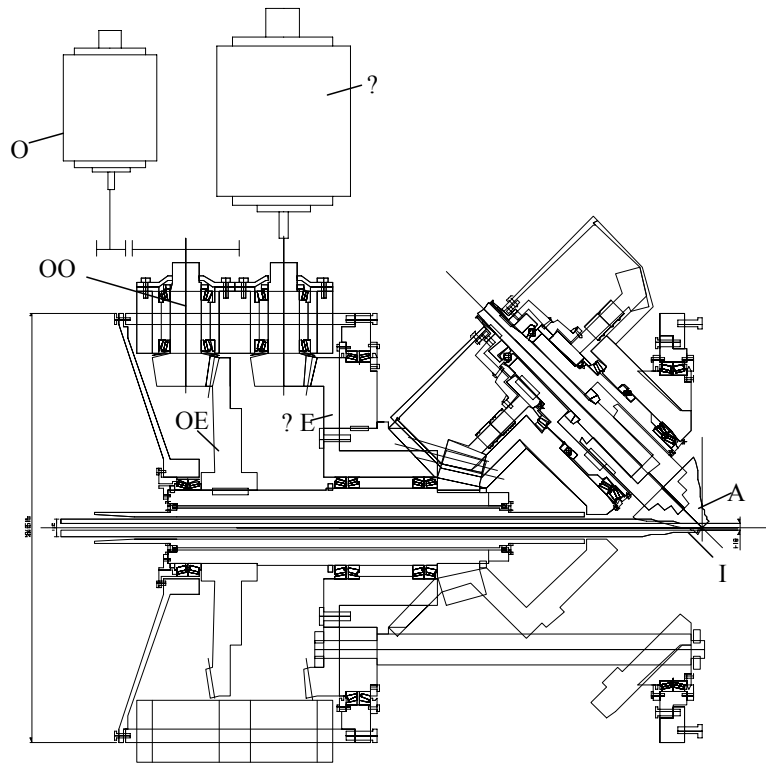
а — Схема конструкции клетки винтовой трехвалковой планетарной консольной обжимной с гипоидной передачей
